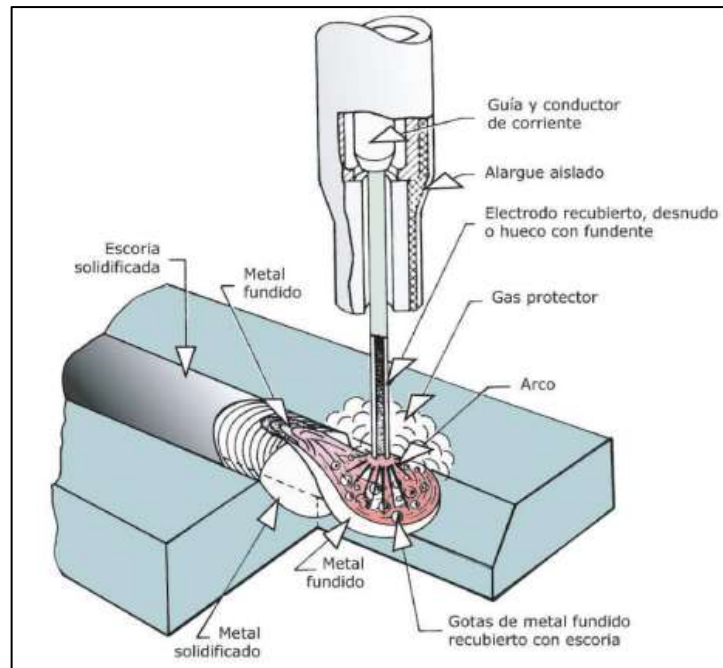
Proceso de fusión en la soldadura MIG
